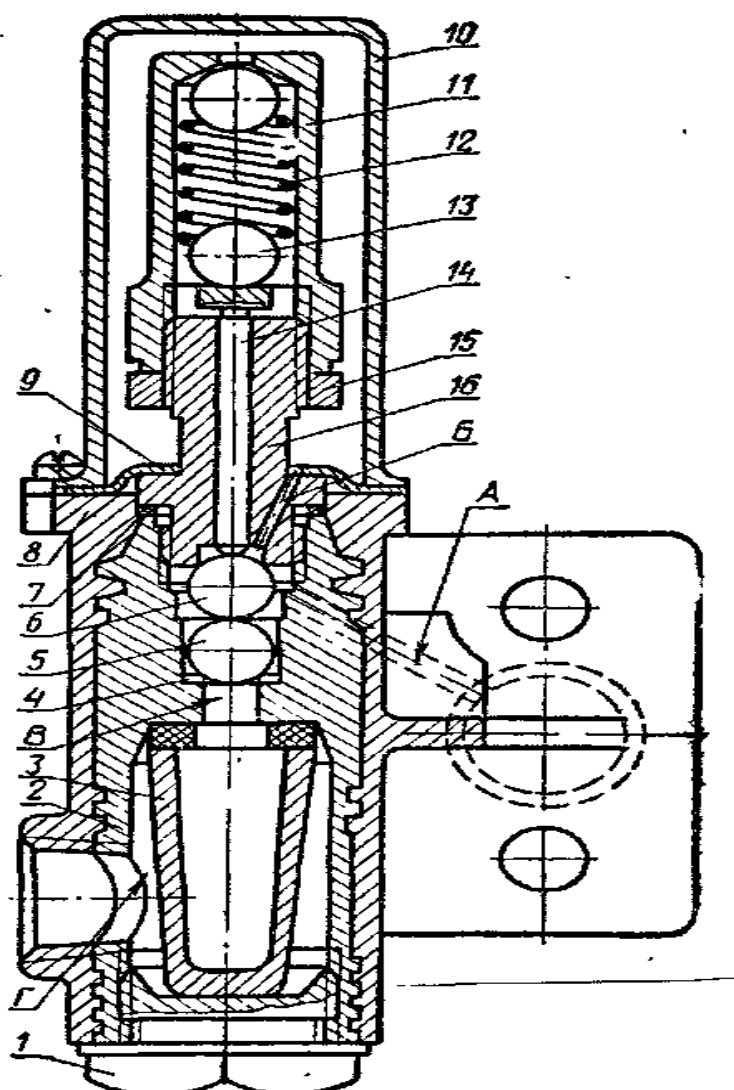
Регулятор давления: 1 – пробка; 2 – втулка; 3 – фильтр; 4 – отжимная шайба; 5 – впускной клапан; 6 – выпускной клапан; 7 – регулировочные шайбы; 8 – корпус; 9 – стопорная шайба; 10 – кожух; 11 – колпачок; 12 – пружина; 13 – шарик пружины; 14 – шток; 15 – контргайка; 16 – седло клапана;
